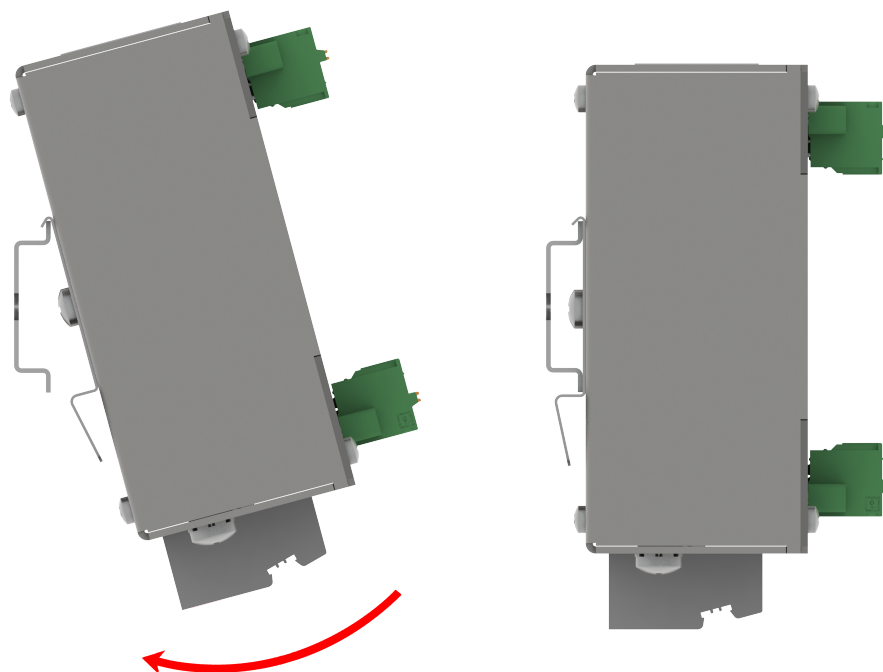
Монтаж устройства на DIN-рейку
